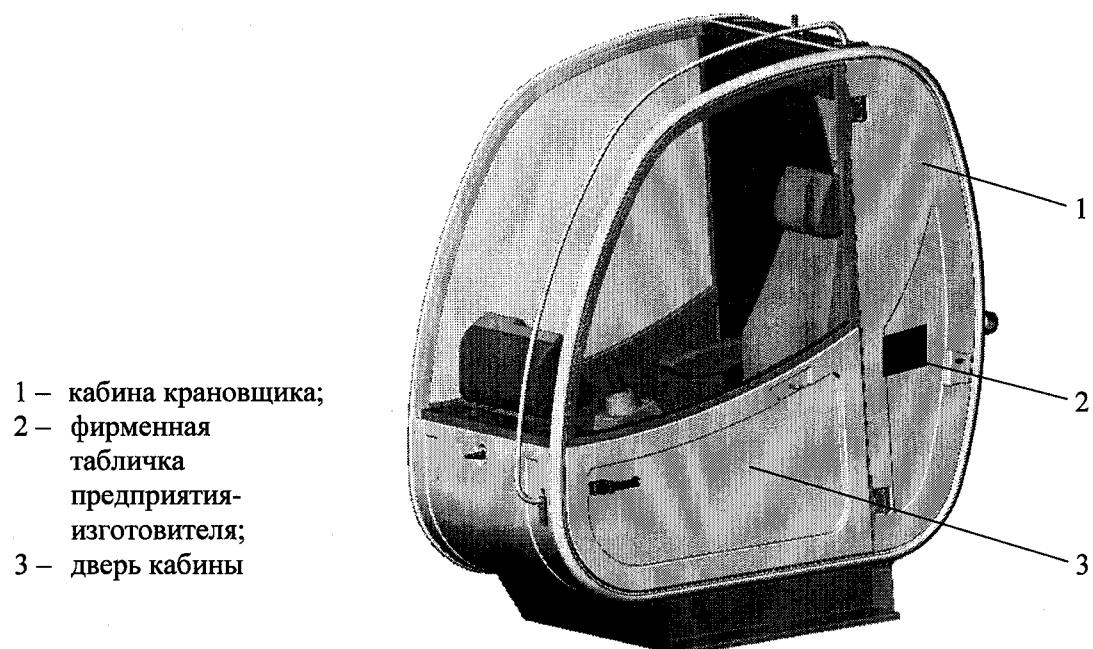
Установка таблички предприятия-изготовителя
